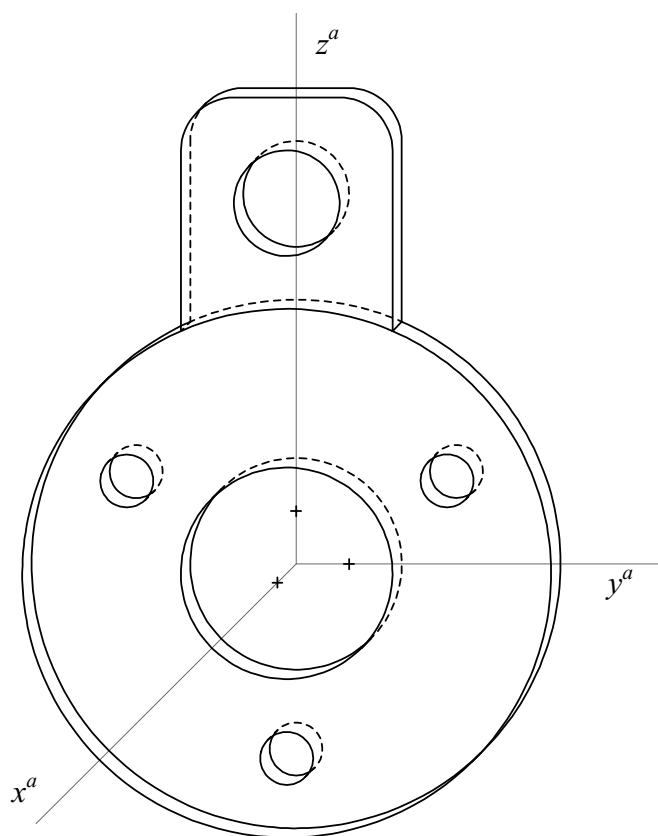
držák zásuvky na tažné zařízení v technické izometrii
